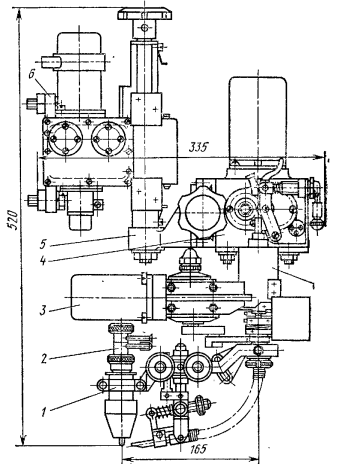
Конструктивная схема подвесной сварочной головки типа АГВ-5: 1 — механизм крепления горелки; 2 — горелка для сварки вольфрамовым электродом; 3 — вибратор; 4 — редуктор для подачи проволоки; 5 — суппорт; 6 — механизм вертикального перемещения; 7 — переходник
